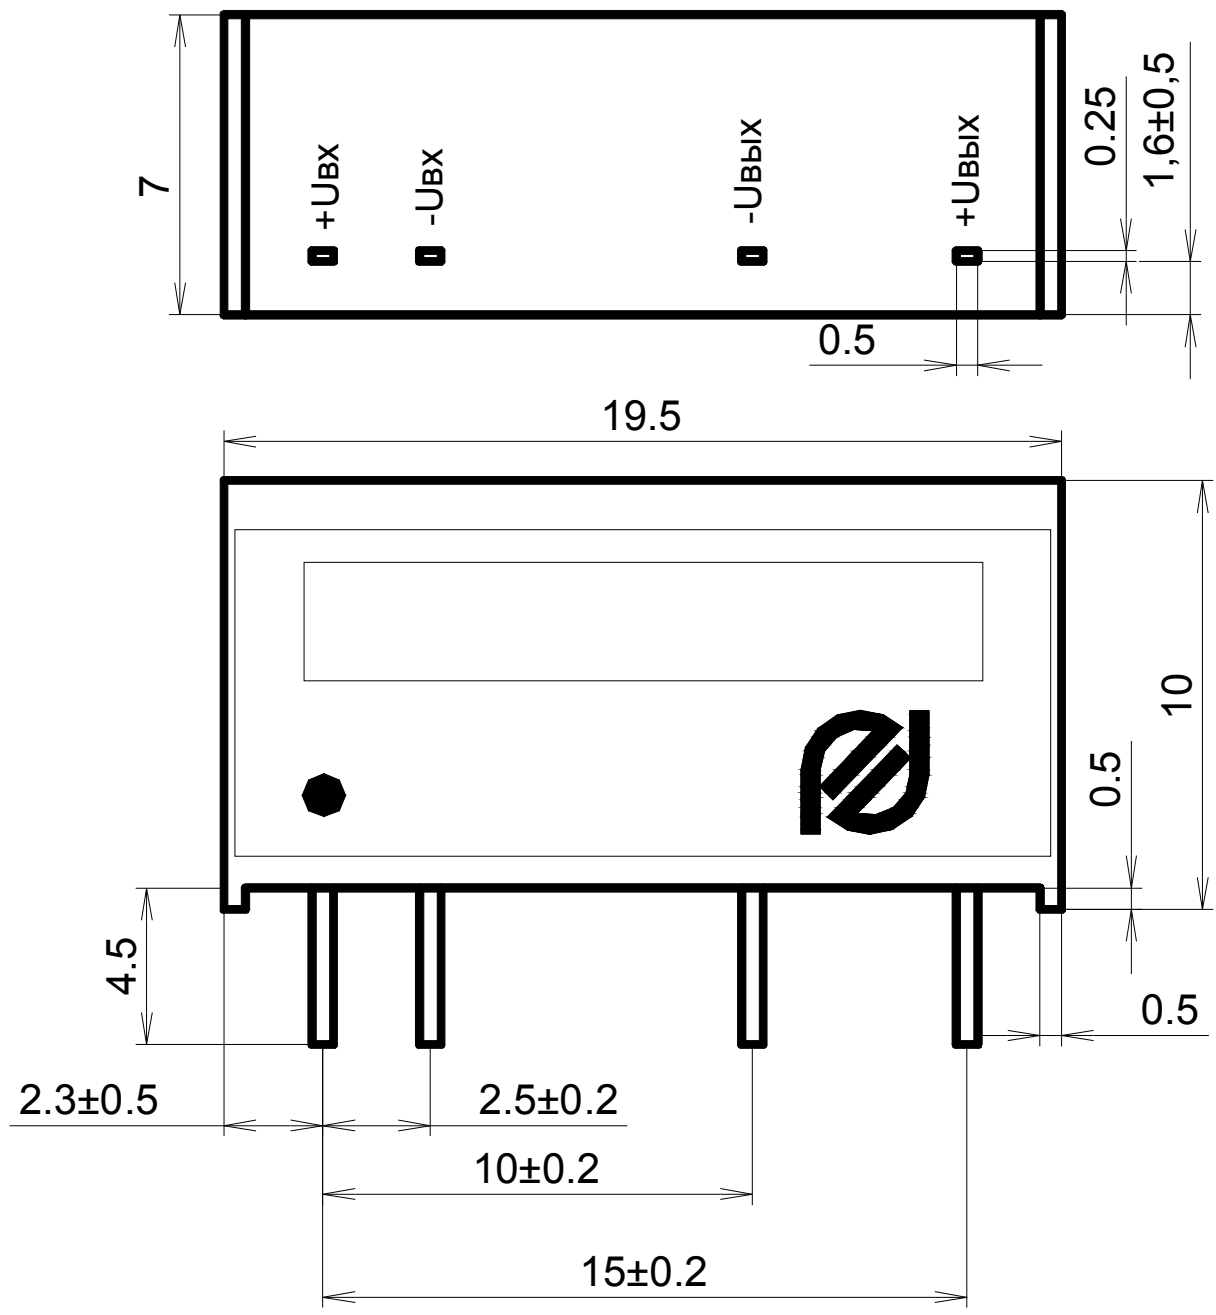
Габаритный чертеж модулей в корпусе «В»
